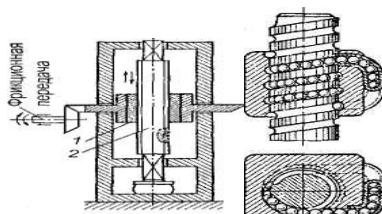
Передача винт-гайка: 1 — гайка; 2 — винт
